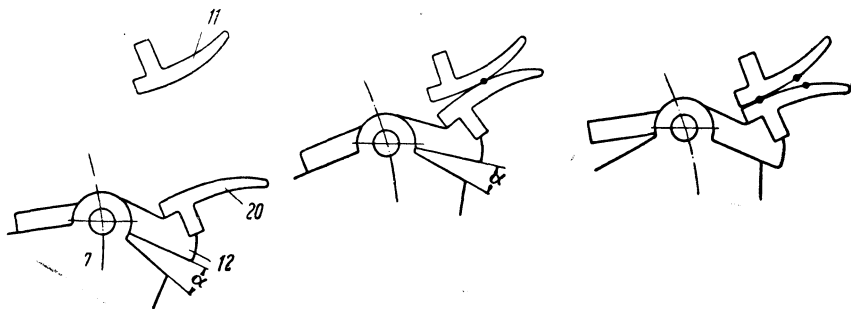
Подвижный контактный механизм контактора типа ПК-301
